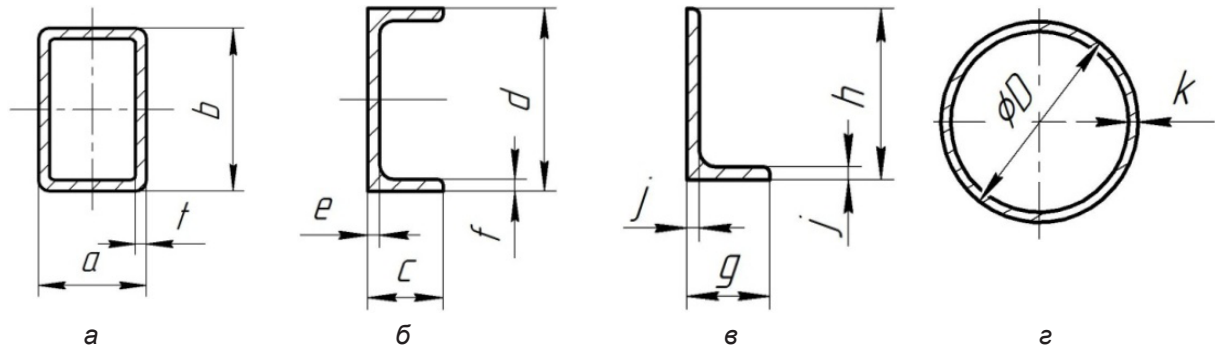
Профили поперечного сечения детали металлоконструкции [16, 17]:
